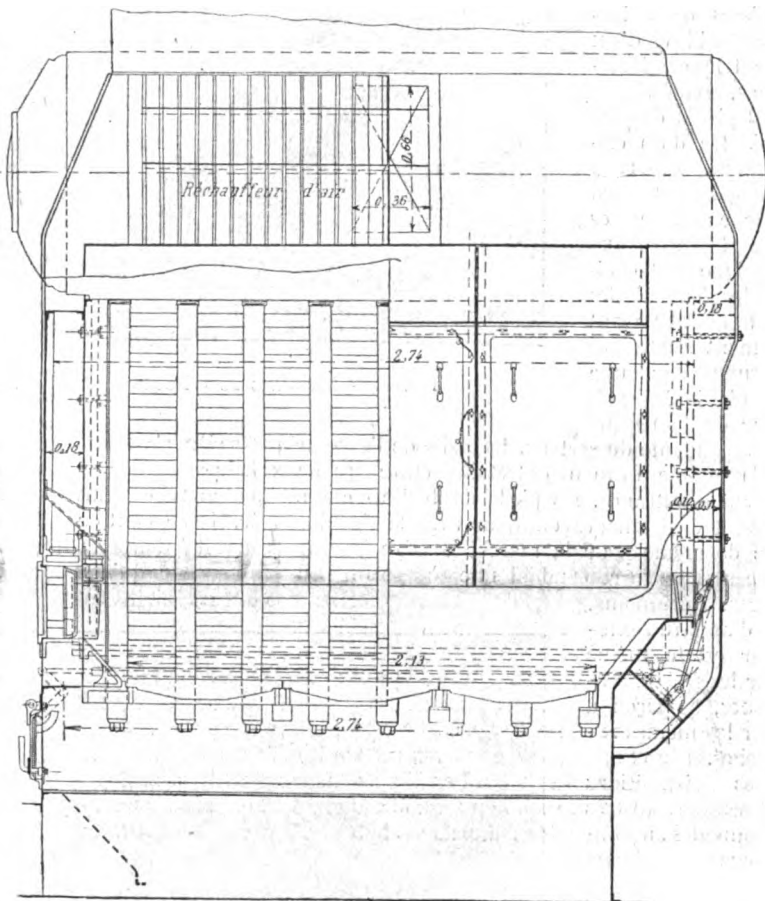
Demi-coupe et demi-élévation longitudinales.
